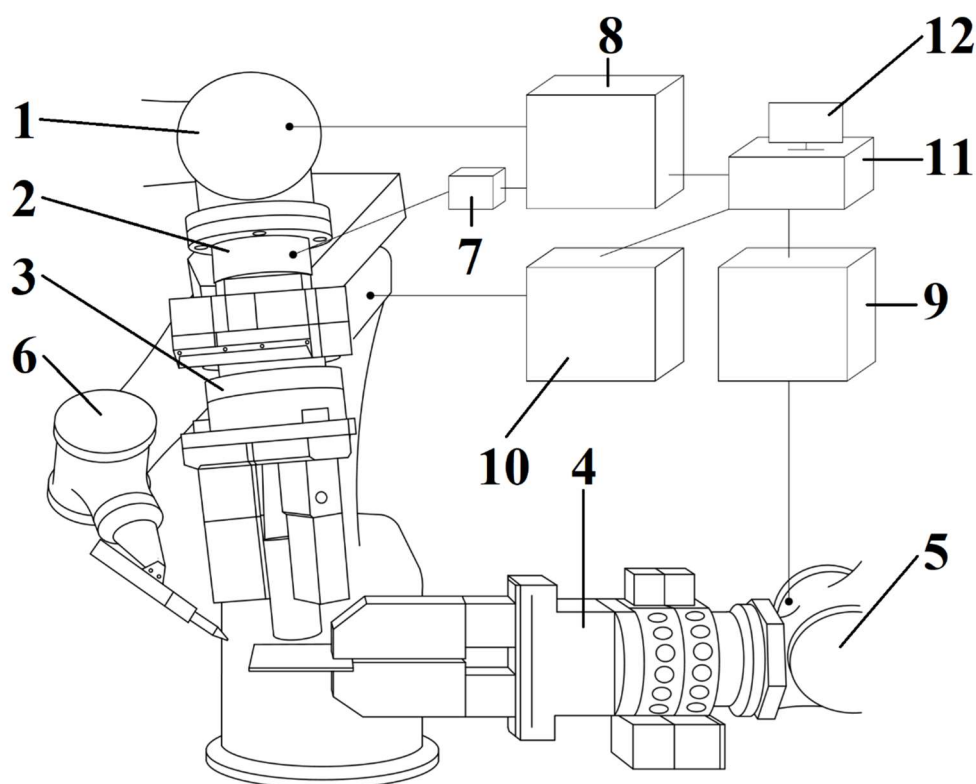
Testovanie automatického rýchlo-výmenného systému robotických chápadiel vo fyzickom prototypu robotického pracoviska
